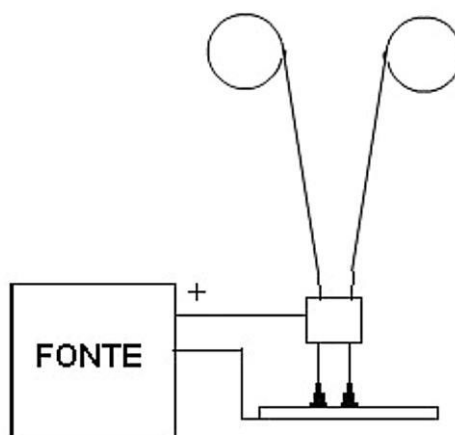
Representação esquemática de um sistema com potencial único conectado à uma fonte de soldagem [13].
